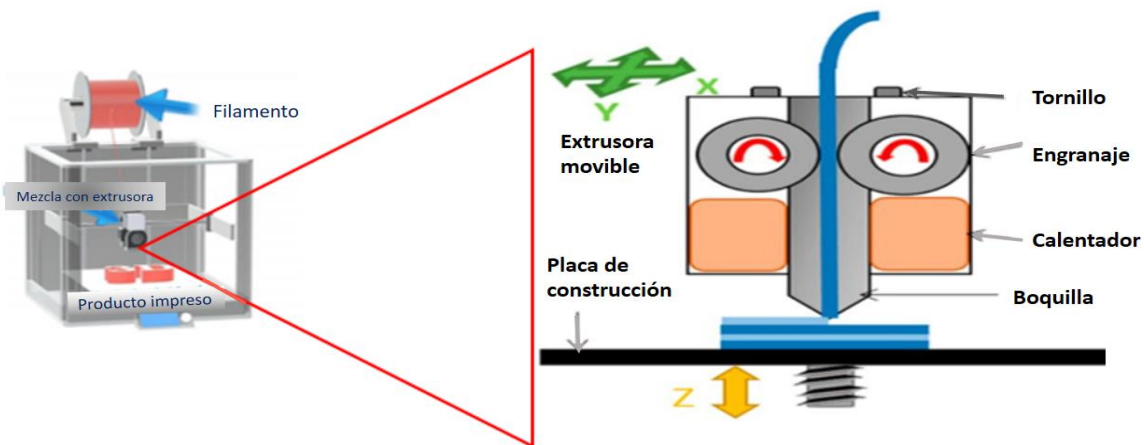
Impresión 3D mediante el método de moldeado por deposición fundida (FDM) (Radacs, 2020).
